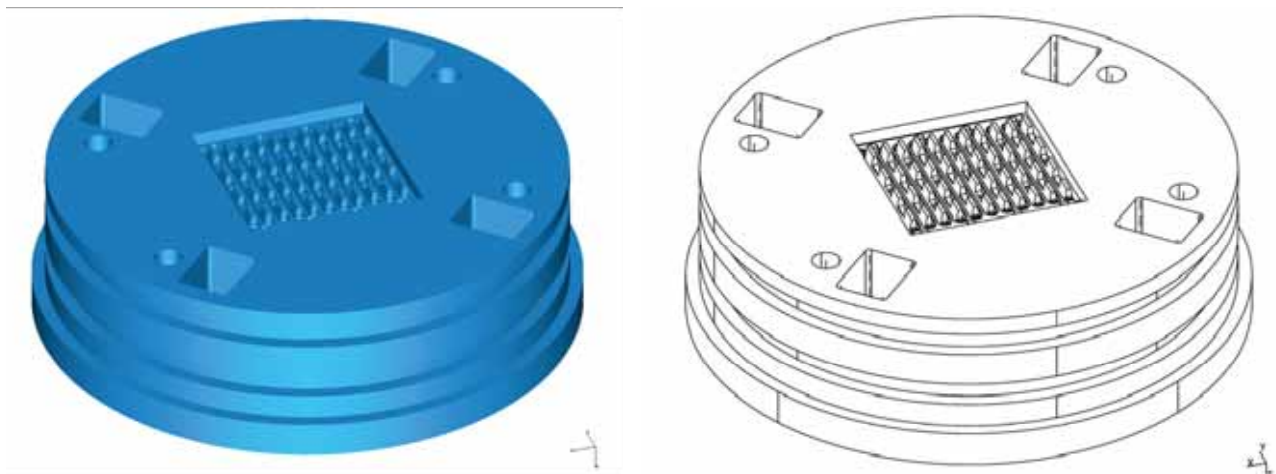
Konstruktionszeichnung der auswerferseitigen Formplatte des Spritzgießwerkzeuges
